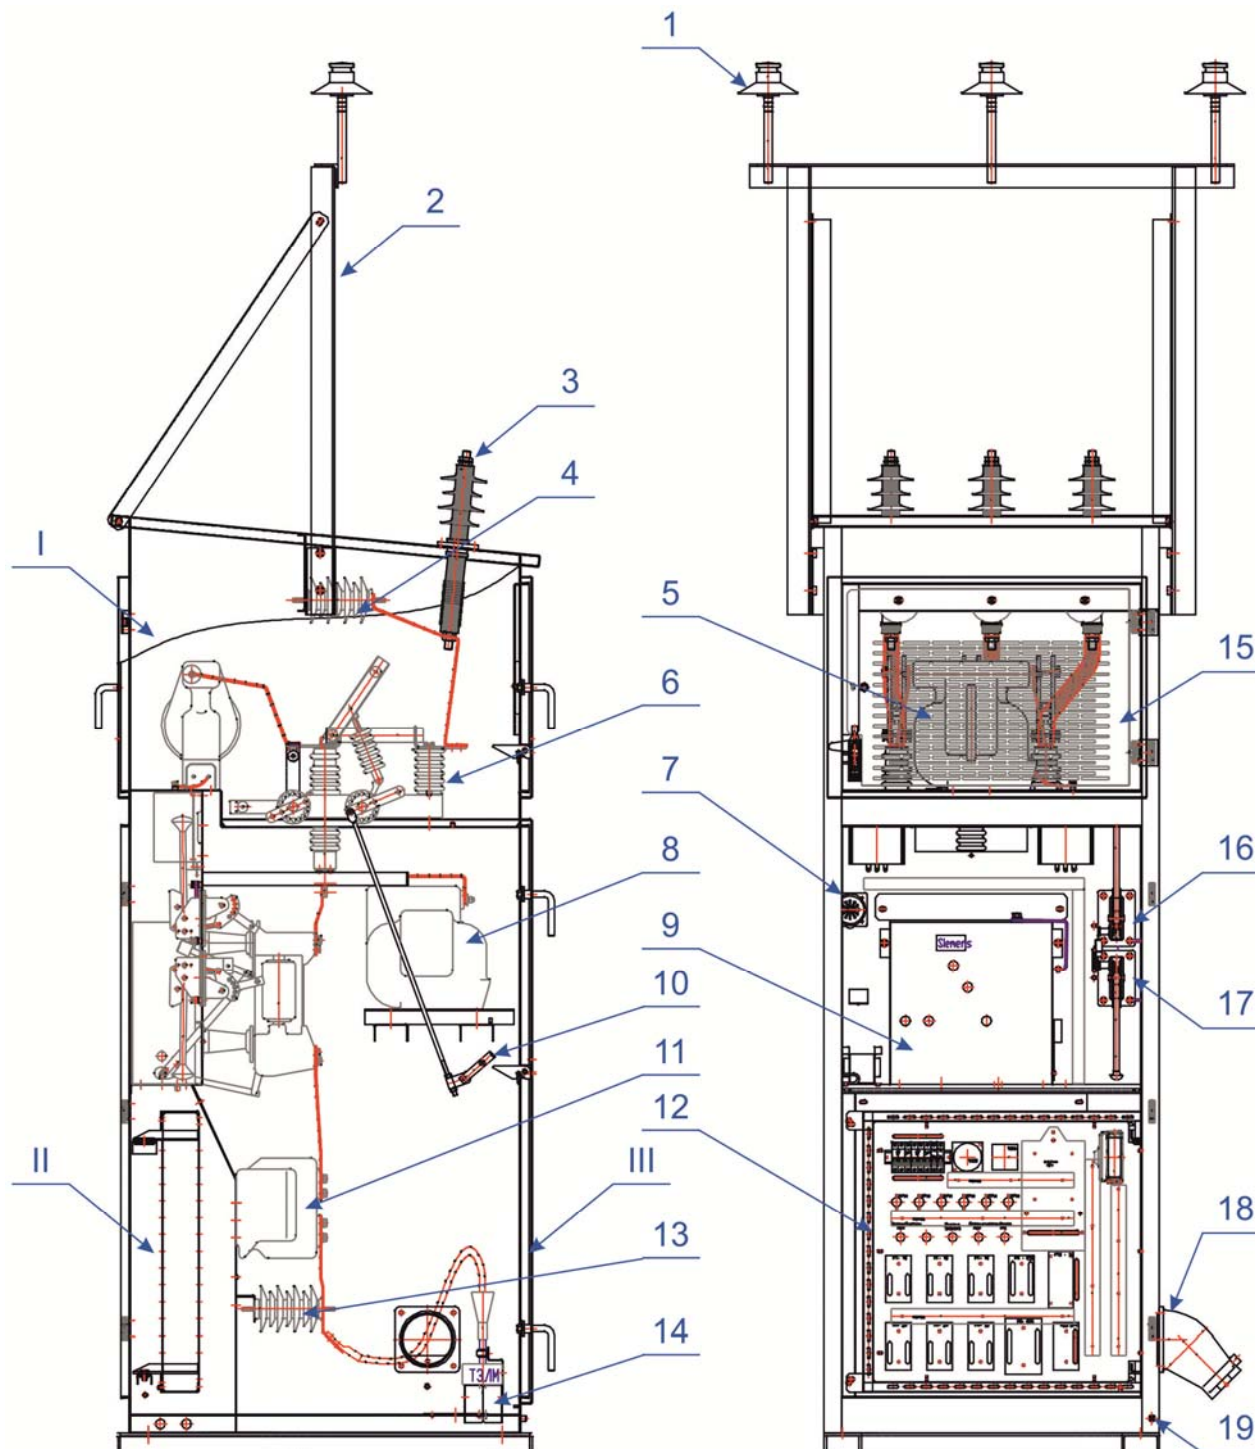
Вид и устройство ЯКНО с вакуумным выключателем SIEMENS
